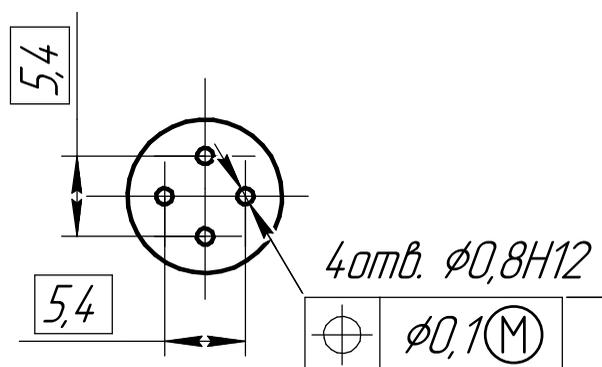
Разметка отверстий для ОСН-25-4/14...П-...
